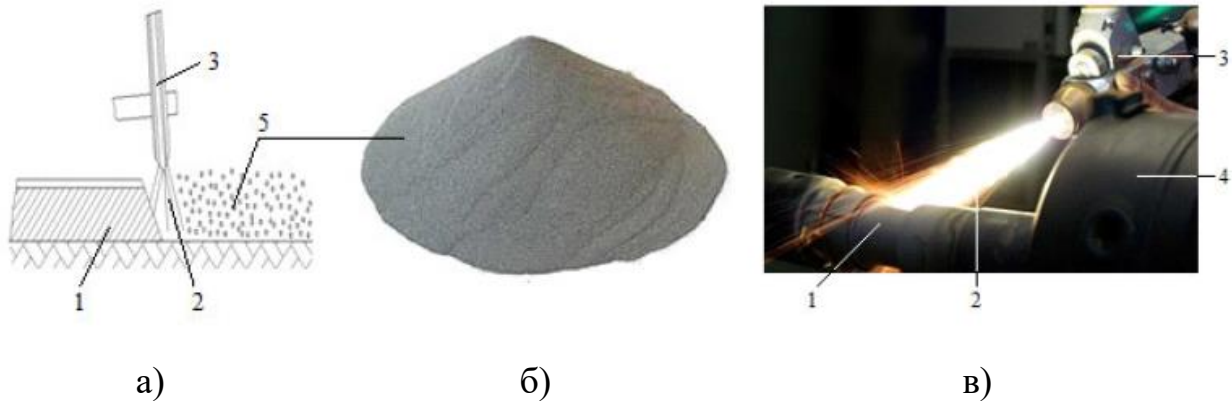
Наплавлення порошкоподібними металами: а – схема наплавлення; б – порошок; в – загальний вигляд наплавлення; 1 – деталь; 2 – плазмова дуга; 3 – плазмотрон; 4 – верстат; 5 – порошок.
